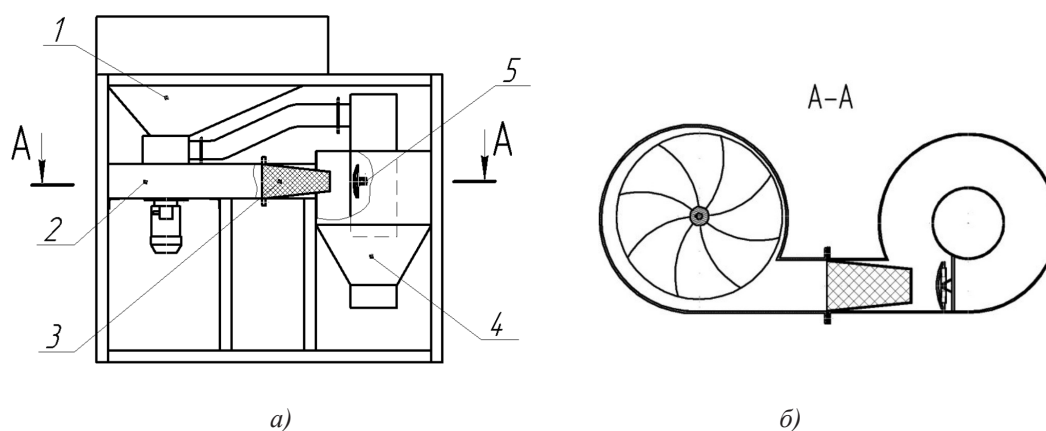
Пневмомеханическое устройство для обрушивания семян подсолнечника: а) – общий вид устройства; б) – разрез А-А; 1 – бункер питающий; 2 – вентилятор; 3 – сетчатый рабочий орган; 4 – осадитель; 5 – сферическая рабочая пластина
